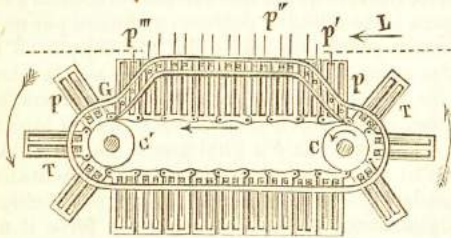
Sbarrette a pettini; disposizione a catena.
